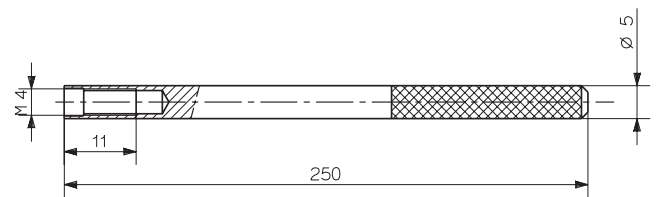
Ausziehwerkzeug für Blindsensor Typ 1319
